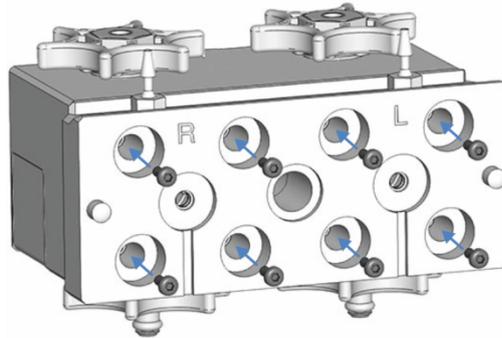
Tête de pompe avec plaque de rinçage des joints and et vis pour plaque
